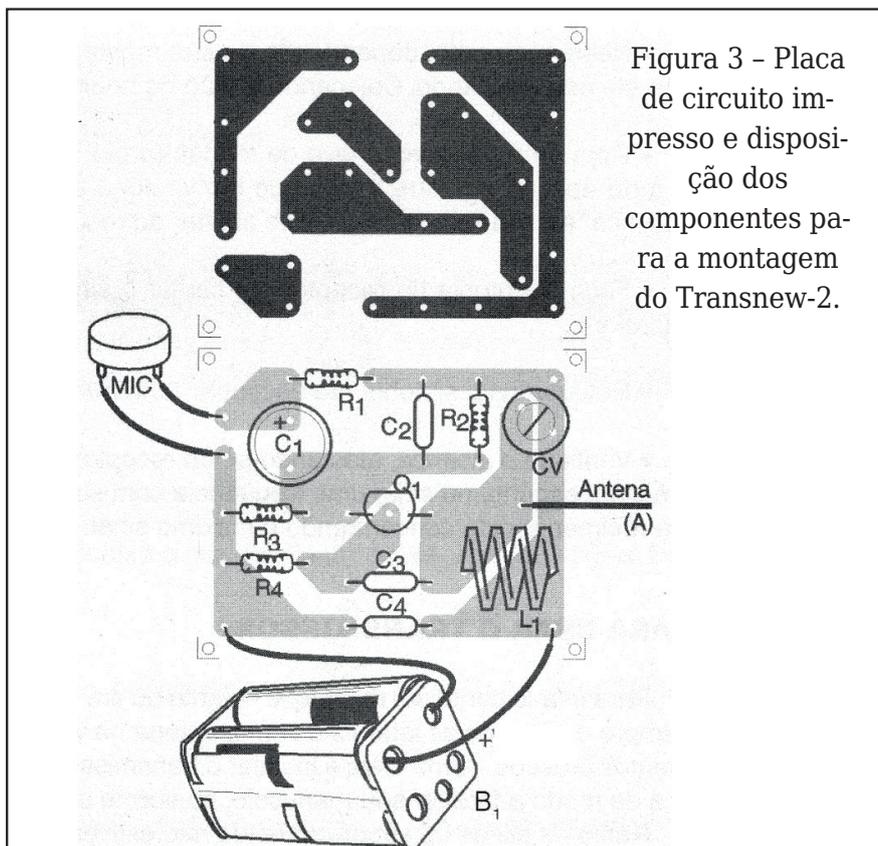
Placa de circuito impresso e disposição dos componentes para a montagem do Transnew-2.
